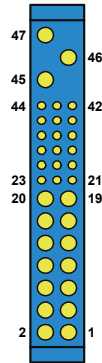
Steckverbinder X0 (P47) (Ansicht: Steckseite)
